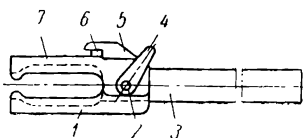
Клещевой патрон: 1 — нижняя челюсть (неподвижная); 2 — ось подвижной челюсти; 3 — штанга-противовес; 4 — рычаг для открытия патрона; 5 — выступ на штанге, под который закладывается планка; 6 — планка; 7 — подвижная челюсть
